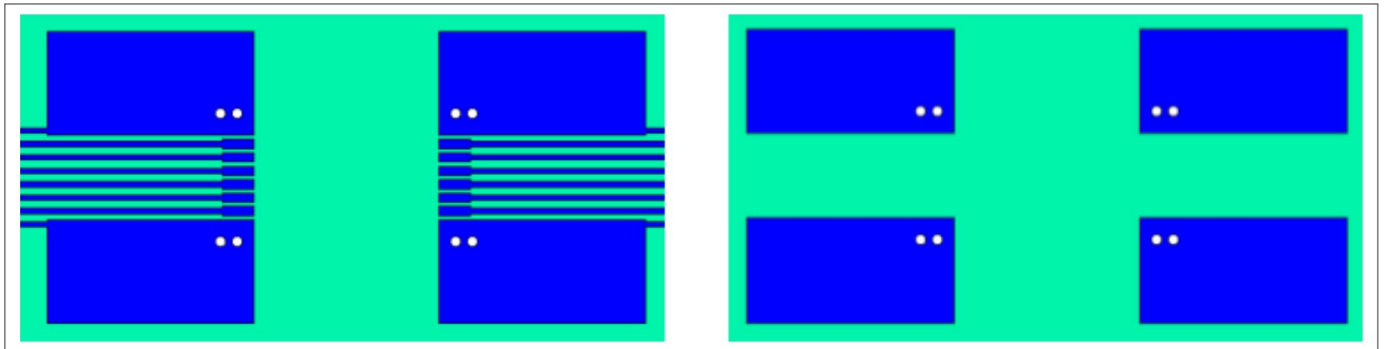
热数据参考布局 (双层 PCB; 铜厚 35 μm; 左: 顶层; 右: 底层)
